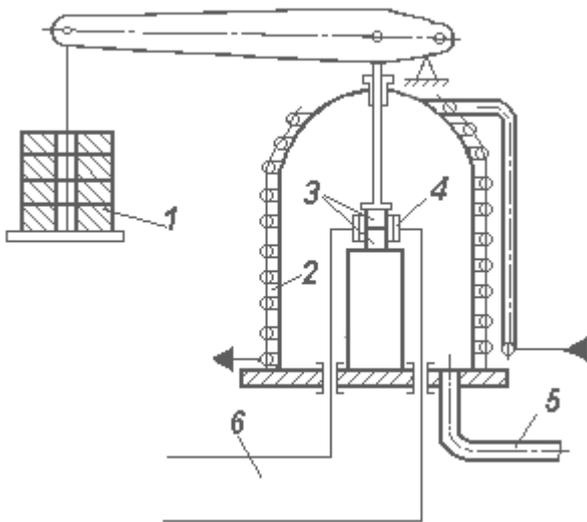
Схема диффузионной сварки в вакууме
